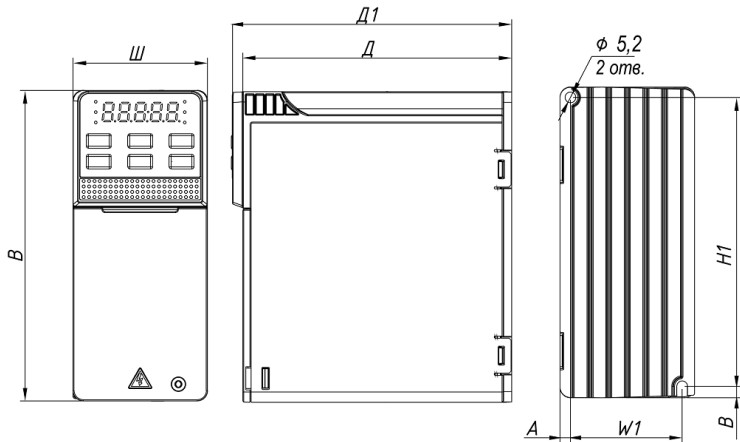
Габаритные и присоединительные размеры (типоразмер 1)
